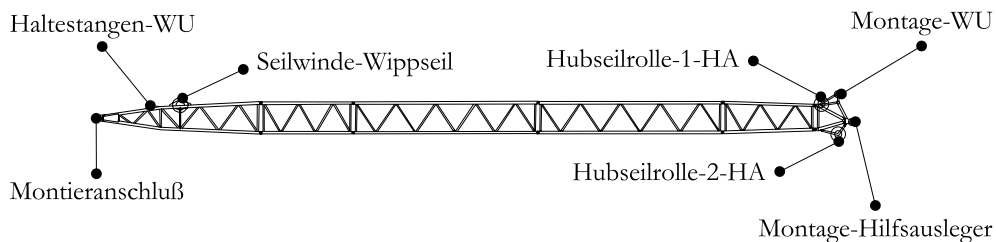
Anschlüsse des Baugruppenprototypen Ausleger
